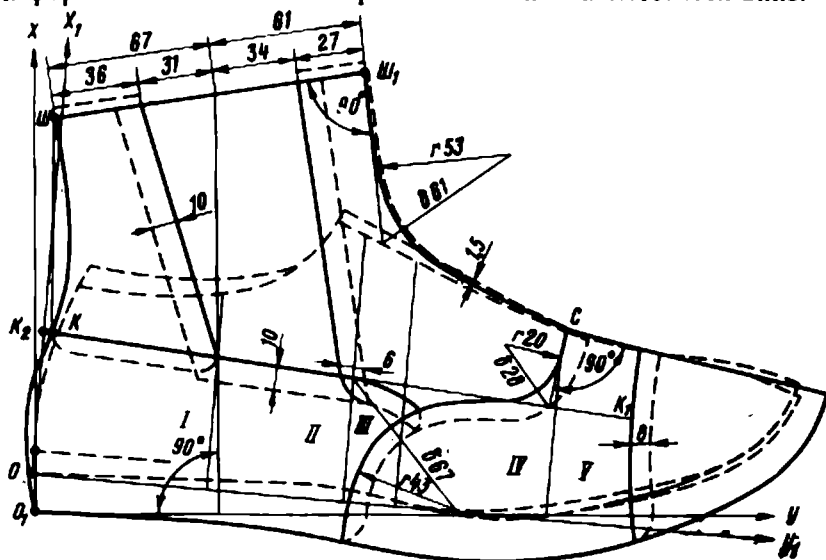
Модель верха мужского ботинка с резинками и отрезными деталями
